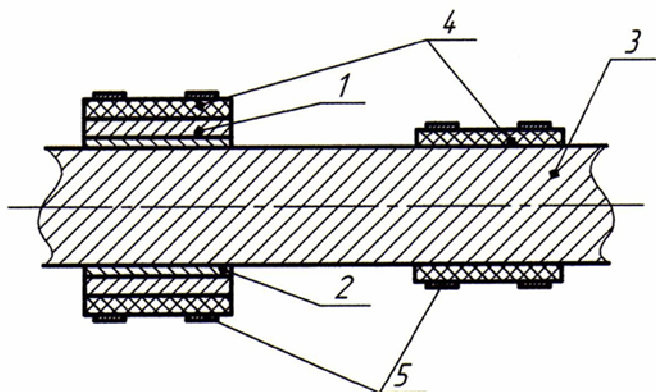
Устройство самоцентрирующегося подшипникового узла скольжения: 1 – корпус подшипника скольжения; 2 – кольцевой вкладыш из немагнитного материала; 3 – валопровод; 4 – постоянные линейные магниты; 5 – хомуты
